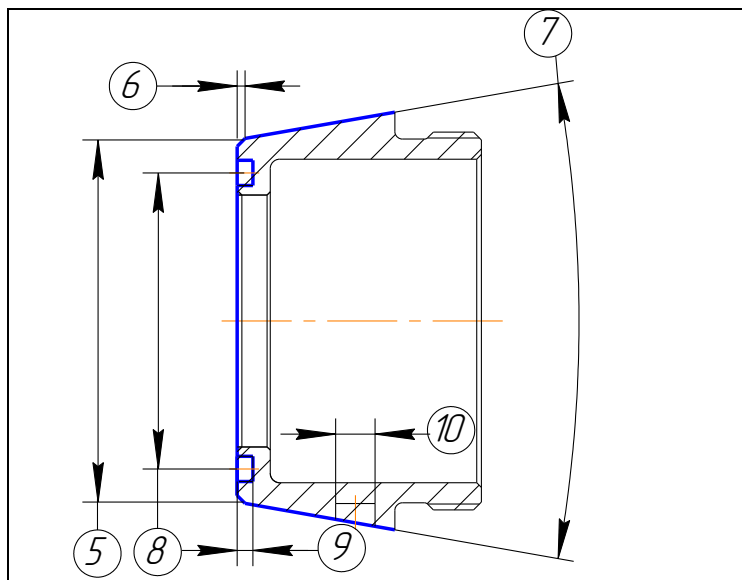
Вигляд заготовки кільця підшипника
